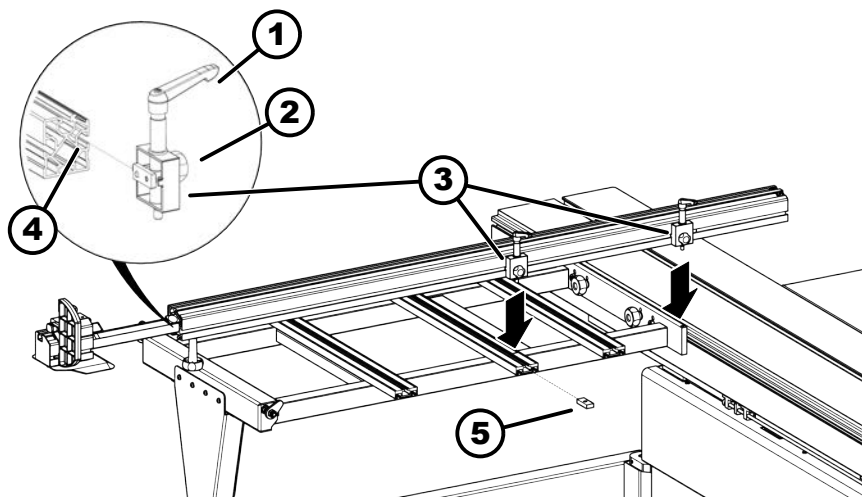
Monter le guide de découpe à la fin de la table coulissante
